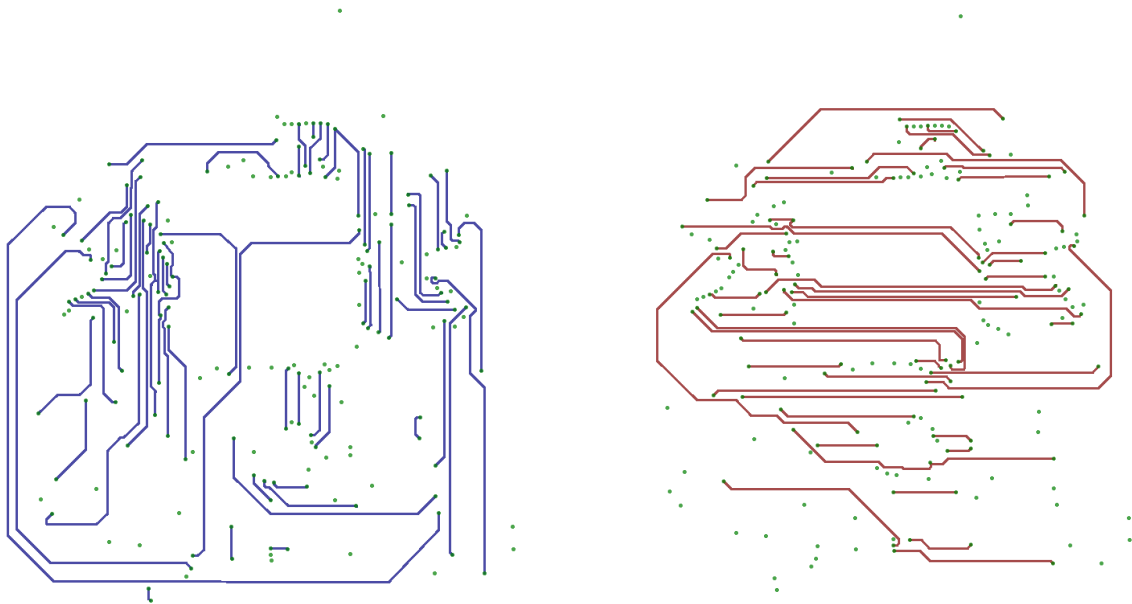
Layout de la primera capa interna con el enrutado en vertical (izquierda) y layout de la segunda capa interna con el enrutado en horizontal (derecha). Fuente: elaboración propia
